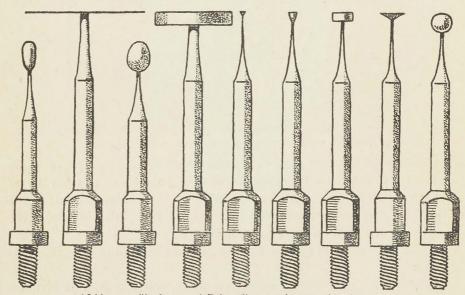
Werkzeuge ("Zeiger") zum Gemmenschneiden.
